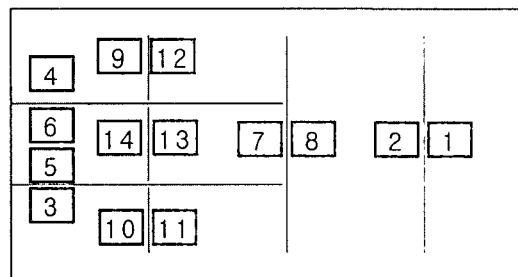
H_Shaped weld path의 형상 및 치수
